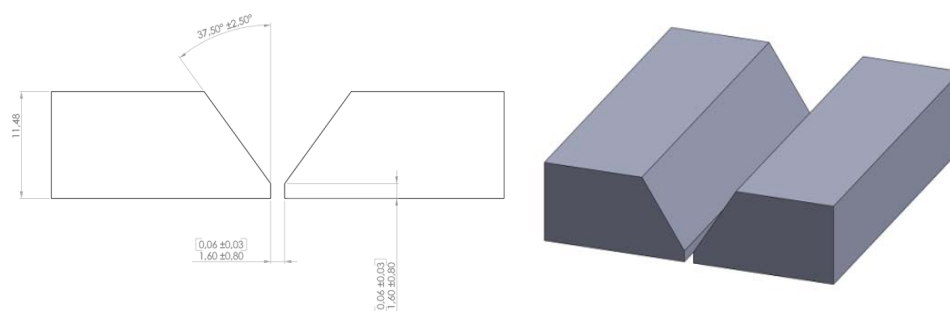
Les pièces à assemblés (Chanfreinage)
